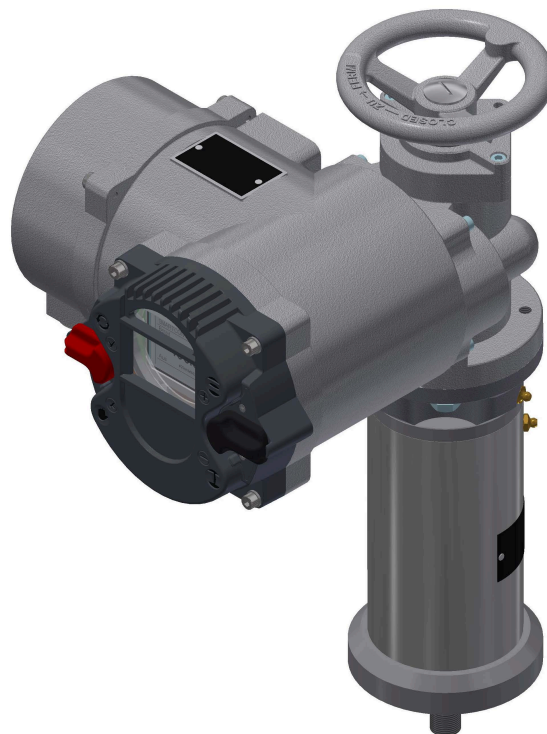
CM03-Antrieb mit aufgebauter LK100-Schubeinheit
